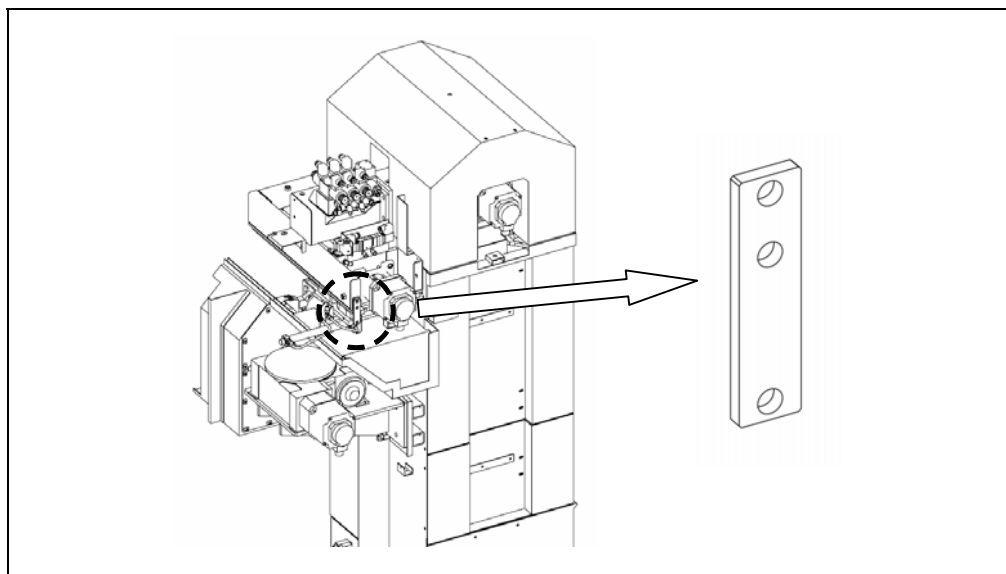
Расположение транспортировочных хомутов – каретка для инструмента
